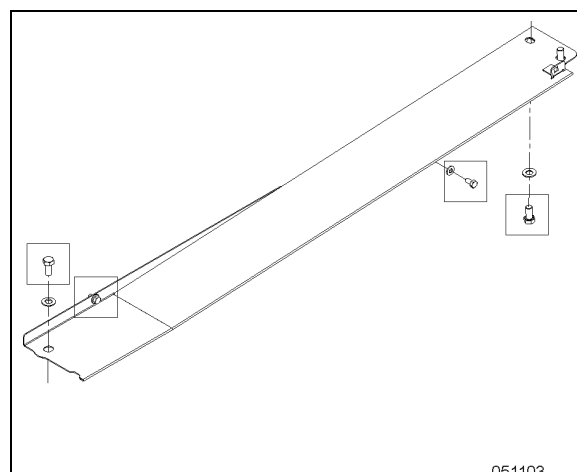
TORNILLOS DE MONTAJE DE LA PLACA PROTECTORA
